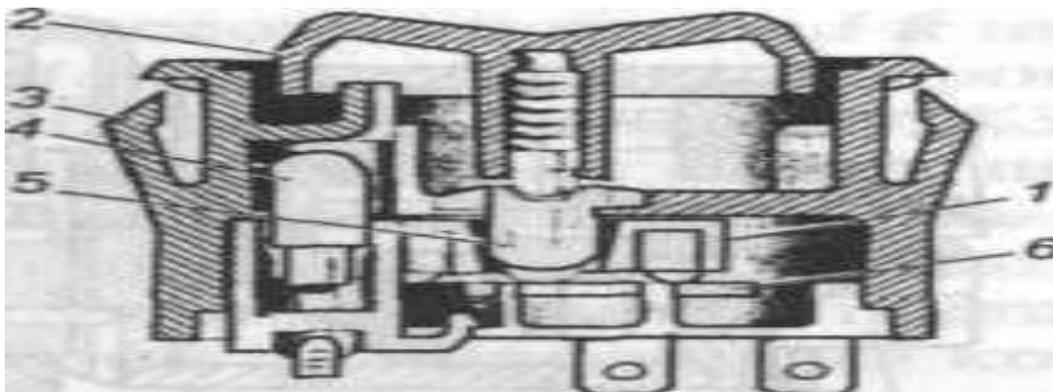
Ползунковый переключатель: 1 — подвижной контакт; 2 — клавиша; 3 — корпус; 4 — лампа подсветки; 5 — перекидная пластина; б — подвижные контакты.
